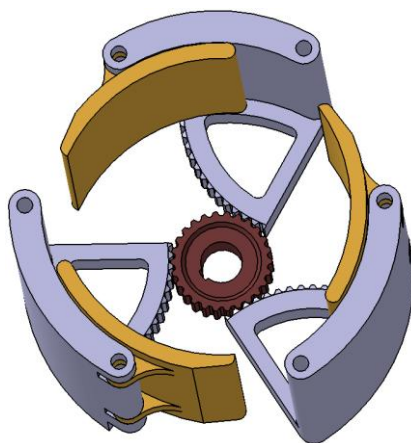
Engrenamento entre roda dentada e braços de transmissão.
